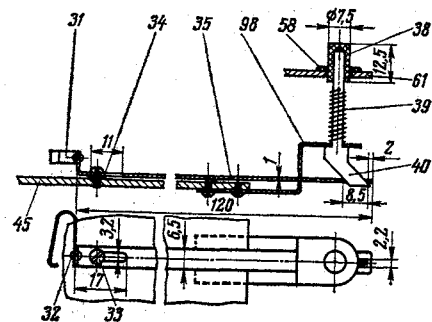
Механизм кнопки «Стоп»: 31 — пружина плоская; 32 — заклепка 2×2; 33 — винт М3×5; 34 — шайба; 35 — толкатель, Ст. 10 кп; 38 — кнопка, эбонит, полировать, ставить на клею БФ-2; 39 — пружина; 40 — планка; 45 — плата; 58 — обрамление, Ст. 20, никелировать; 61 — панель; 98 — кронштейн.
